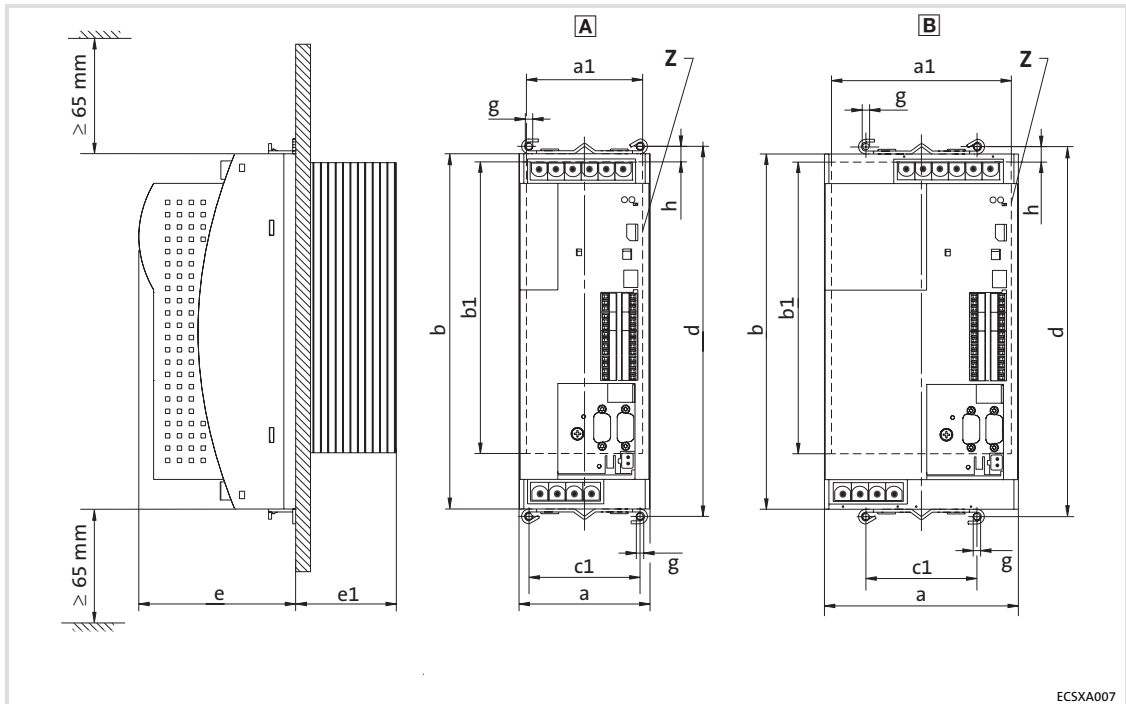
Dimensiones con el formato "Técnica de perforación"
